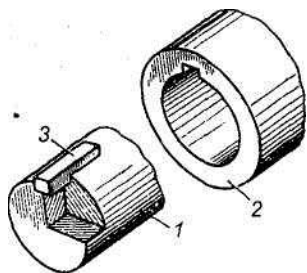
Соединение шпонкой: 1 — вал; 2 — ступица; 3 — шпонка
